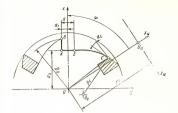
Профиль винтовой канавки концевой фрезы под винтовые пластинки из твердого сплава
